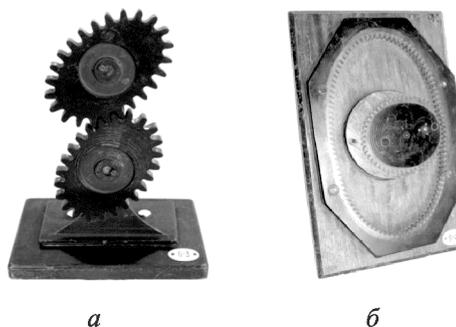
Модели G03 (а) и G04 (б) передач с некруглыми колесами с внешним и внутренним зацеплением
